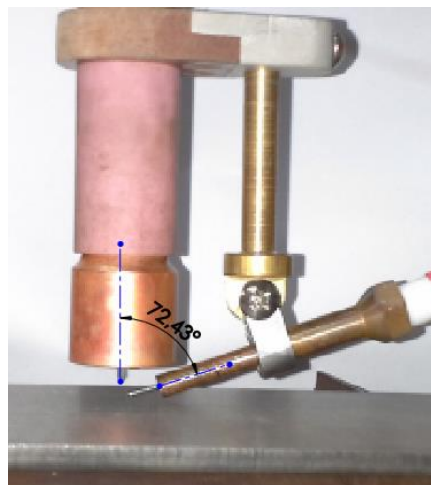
Dispositivo de Teflon utilizado para evitar aquecimento demasiado do Conduíte
